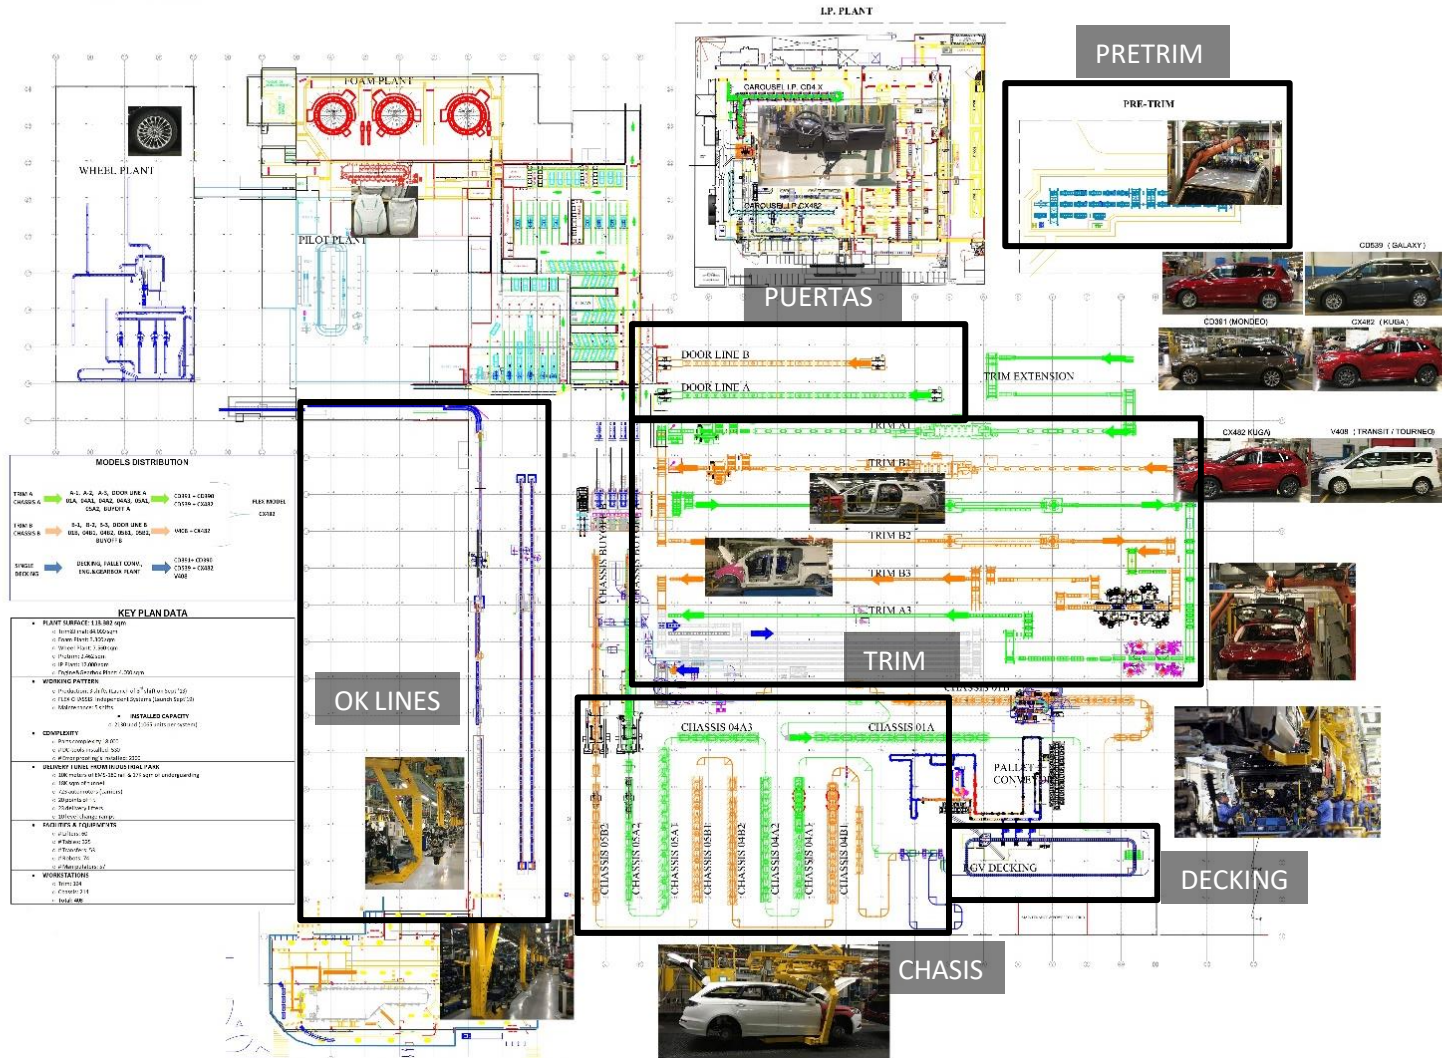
Layout Planta Montaje (Fuente: Documentos Ford)
